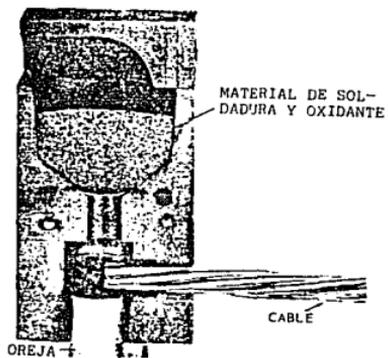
Partes de cables para soldar siendo unidas mediante el proceso de soldadura aluminotérmica.
